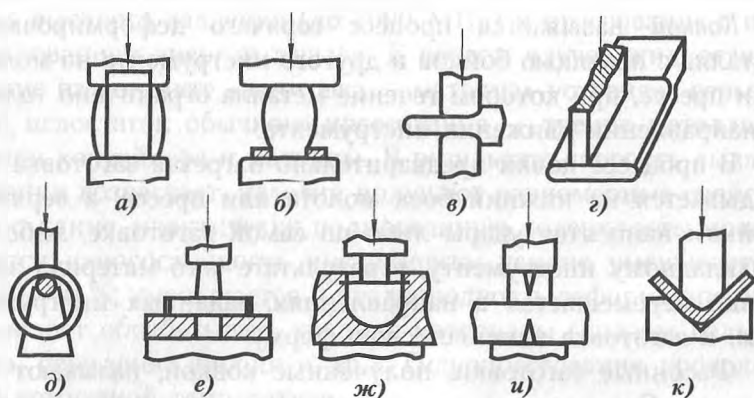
Операции ковки: а — осадка; б — высадка; в — протяжка; г — разгонка; д — раскатка; е и ж — прошивка; и — отрубка; к — гибка
